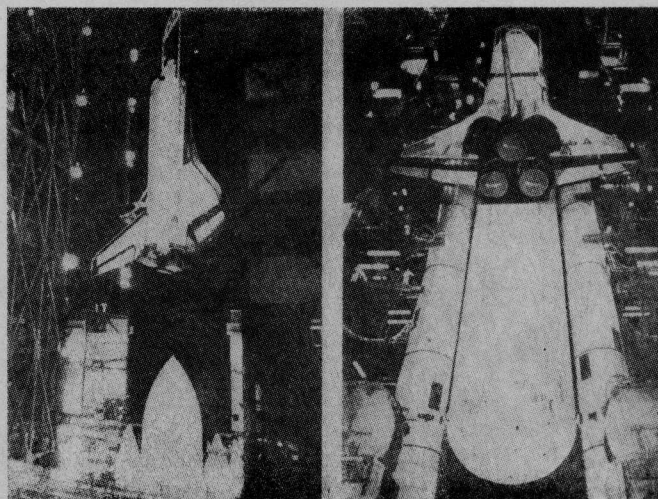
Стыковка ВКС «Колумбия» с внешним топливным баком в корпусе вертикальной сборки космического центра им. Кеннеди
